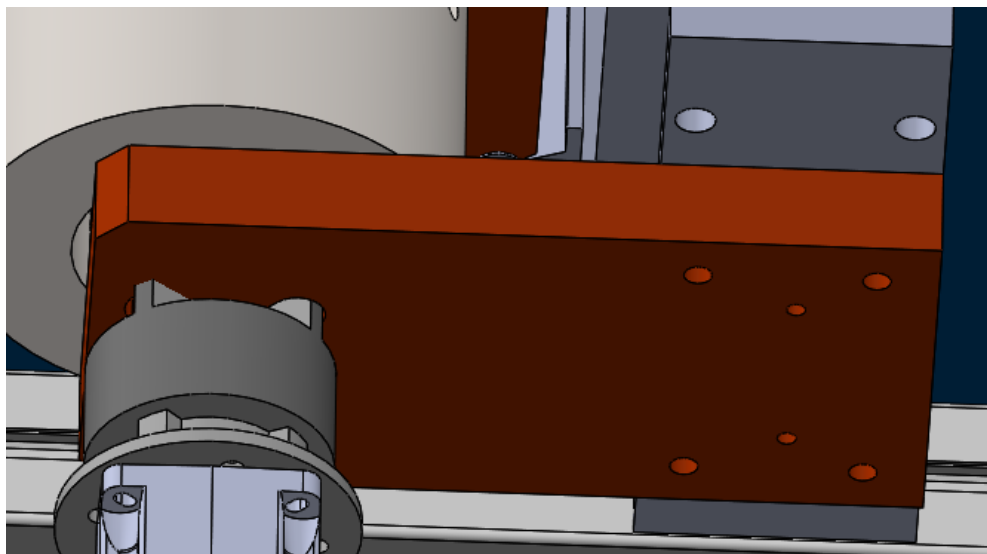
Fixação do Apoio – Redutor – Solução Final
